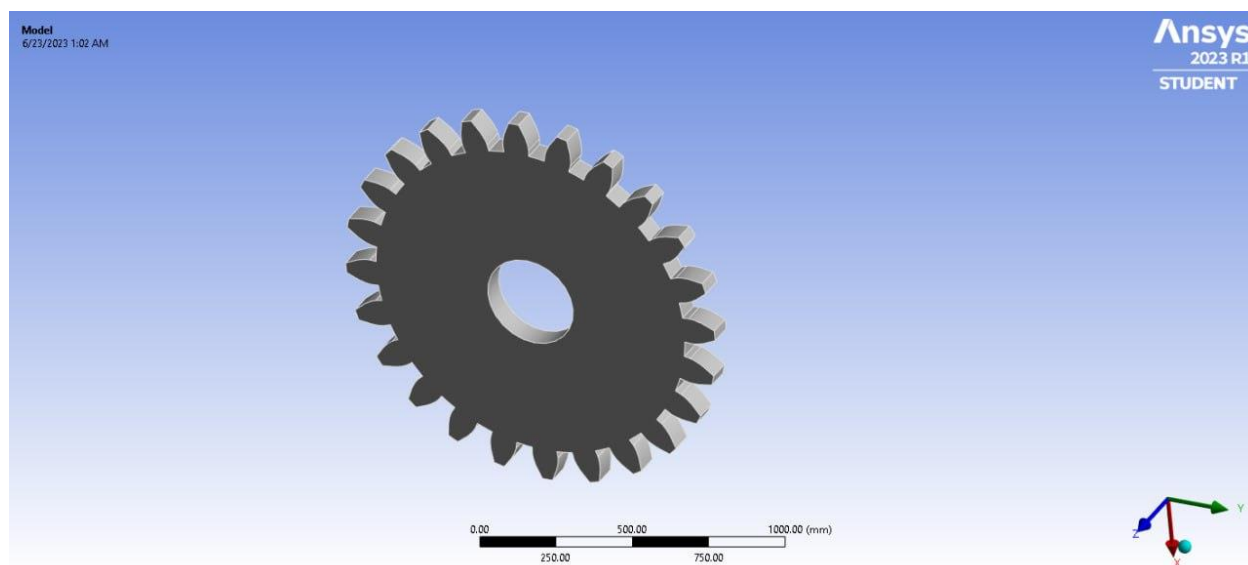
3D модель зубчатого корпусу приводу дробарки
